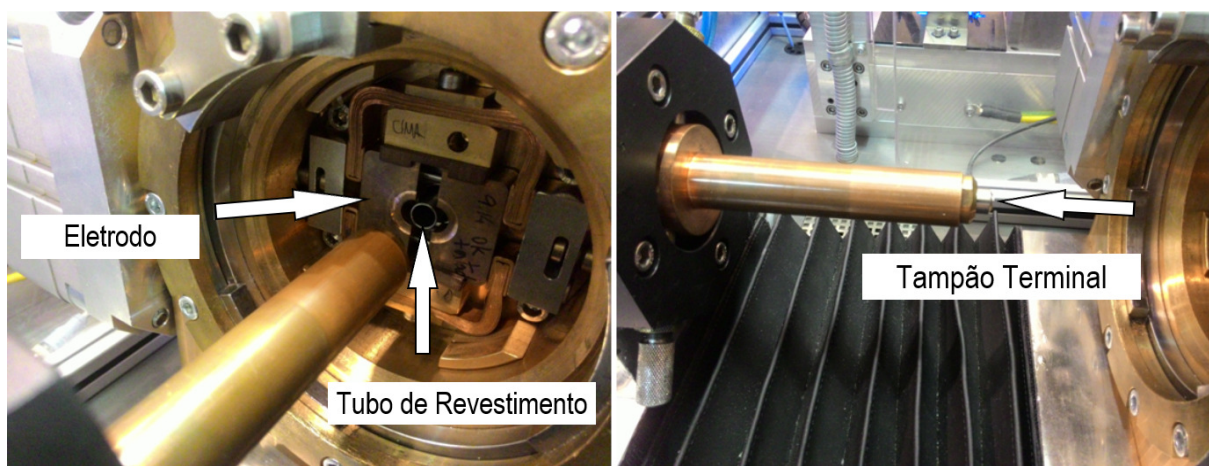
Imagem da câmara de soldagem por resistência e pressão
